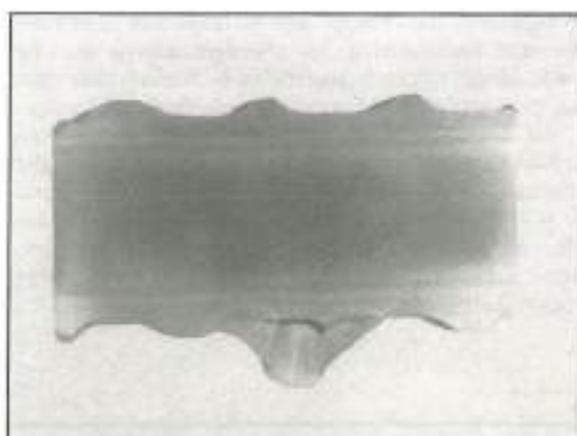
Macrografía de una soldadura en cruz.
